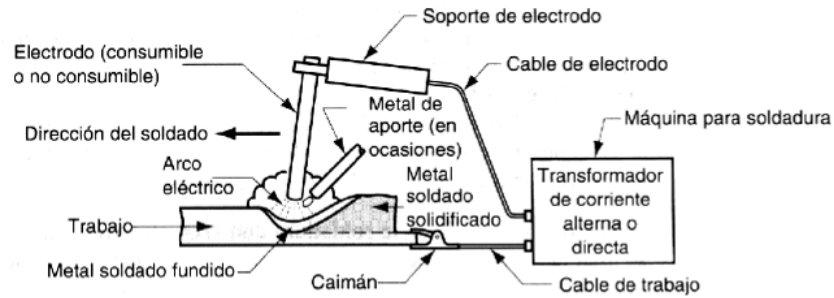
Esquema del proceso de realización de la unión soldada [27].
